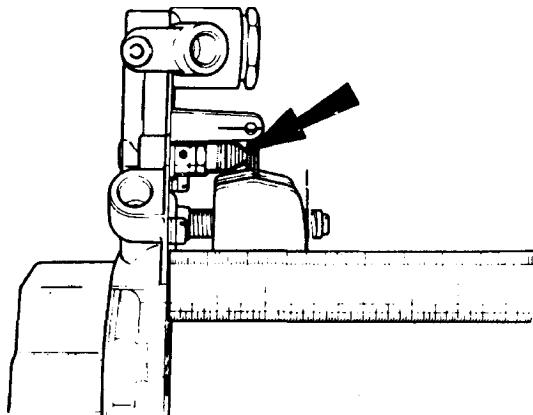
Язычок регулировки уровня поплавка - карбюратор WEBER.
